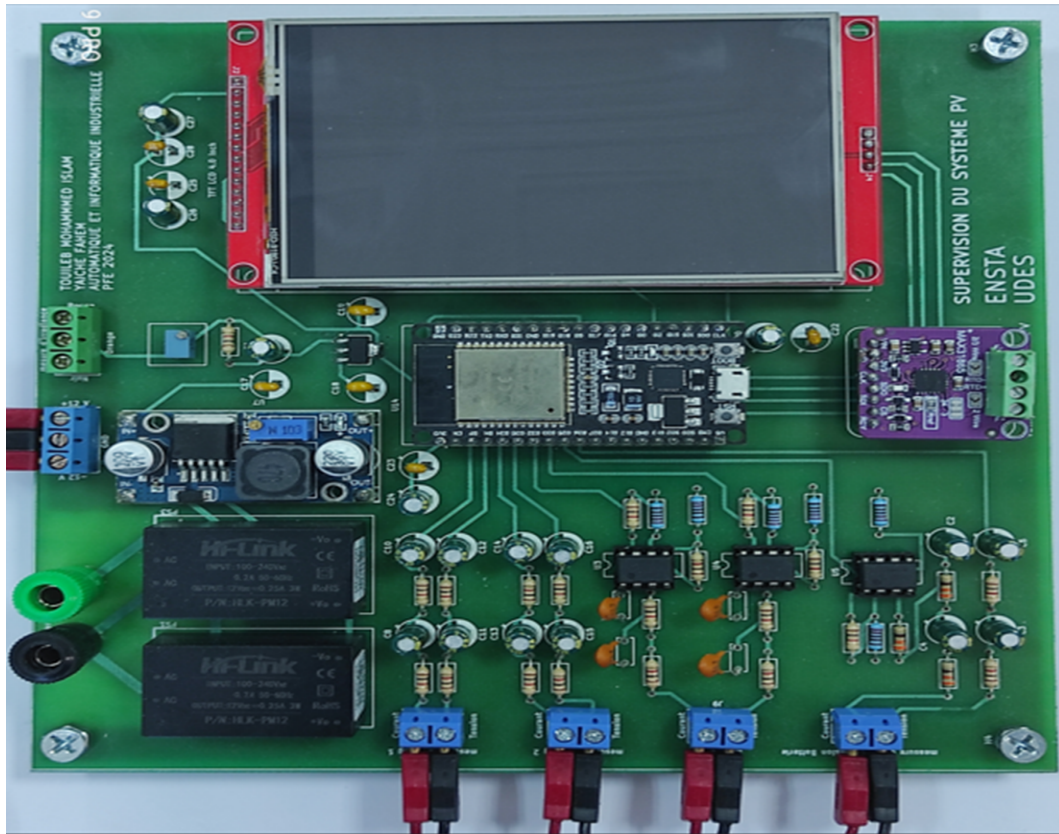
Vue de la carte principale finie dimension 175x172 mm
